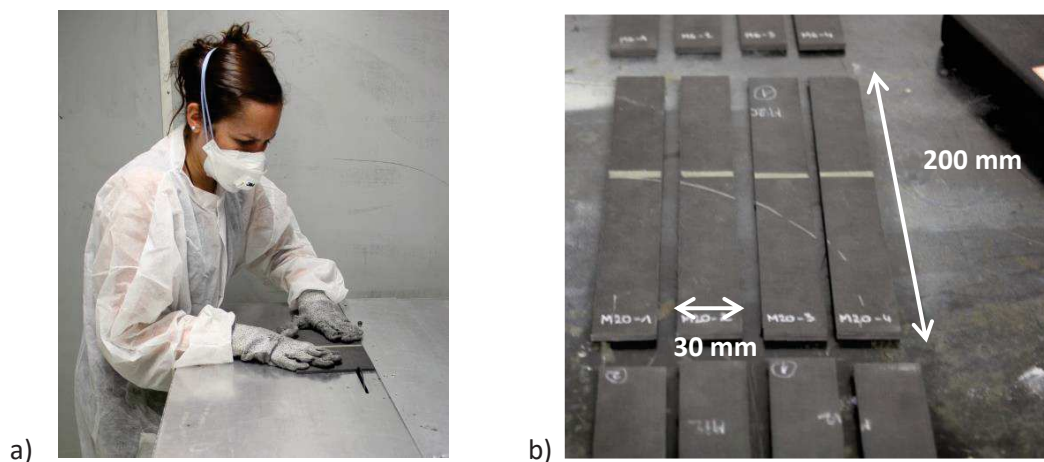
Découpe finale des éprouvettes avec a) phase de découpe en cours et b) vue globale des éprouvettes simple marche assemblées par collage
